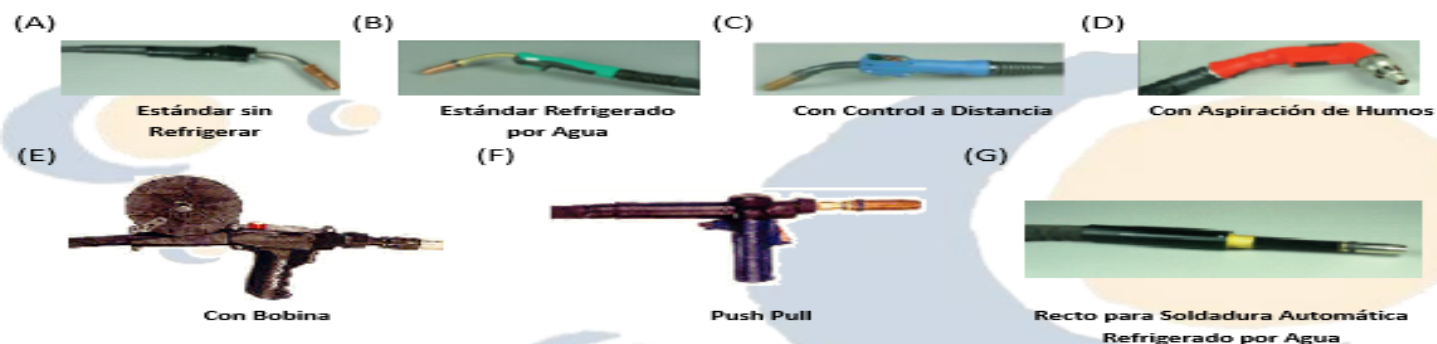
Diferentes tipos de sopletes MIG (A) Estándar sin refrigerar, (B) estándar refrigerado por agua, (C) con control a distancia, (D) Con aspiración de humos, (E) con bobinas, (F) Push Pull y (G) recto para soldadura automática refrigerado por agua
